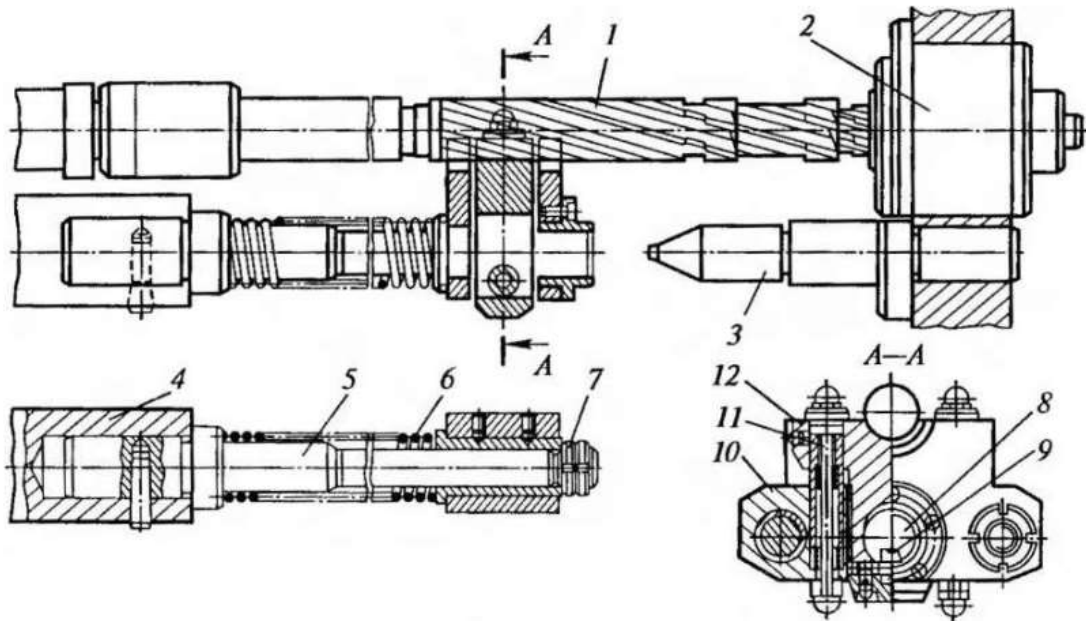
Інструментальний пристрій у вигляді підтримки на агрегатному верстаті барабанного типу: 1 – ріжучий інструмент; 2 – втулка; 3 – конусний штир; 4 – шпindelна коробка; 5 – штанга; 6 – пружина; 7 – регульовальна гайка; 8 – вісь; 9 – ролик; 10 – підтримка; 11 – качалка; 12 – корпус підтримки
